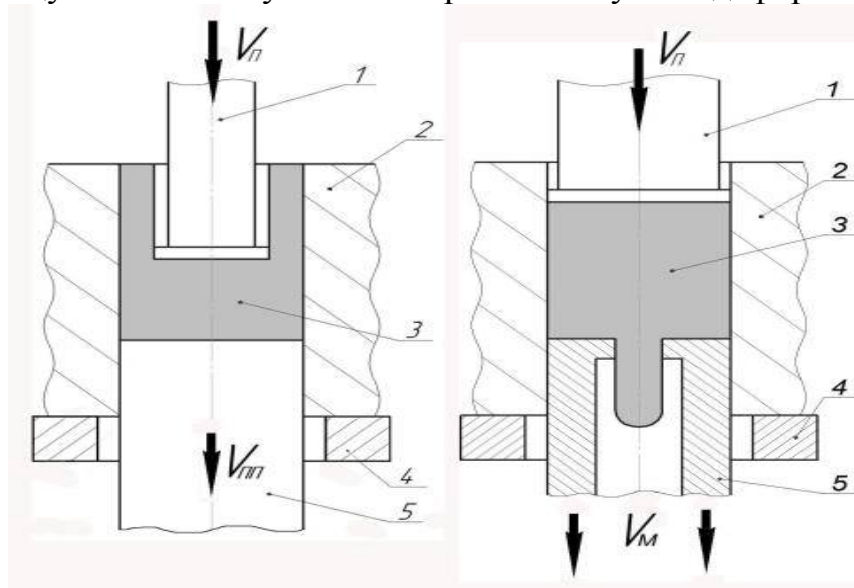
Схеми зворотного видавлювання полого виробу (а) і пресування прутка (б) з активною дією сил тертя: 1 - пуансон; 2 - контейнер; 3 - заготовка; 4 - плита; 5 - протівопуансон; 6 - матриця
